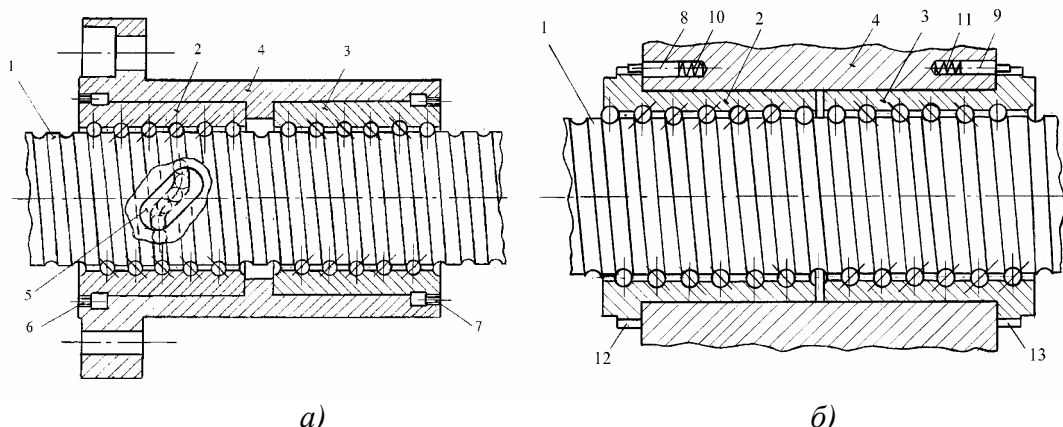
Конструкция шарико-винтовой передачи с возвратом шариков через вкладыши: 1-винт; 2, 3-полугайки; 4-корпус; 5-вкладыш; 6, 7-зубчатые венцы; 8, 9-фиксирующие штифты; 10, 11-пружины; 12, 13-полукруглые впадины.
